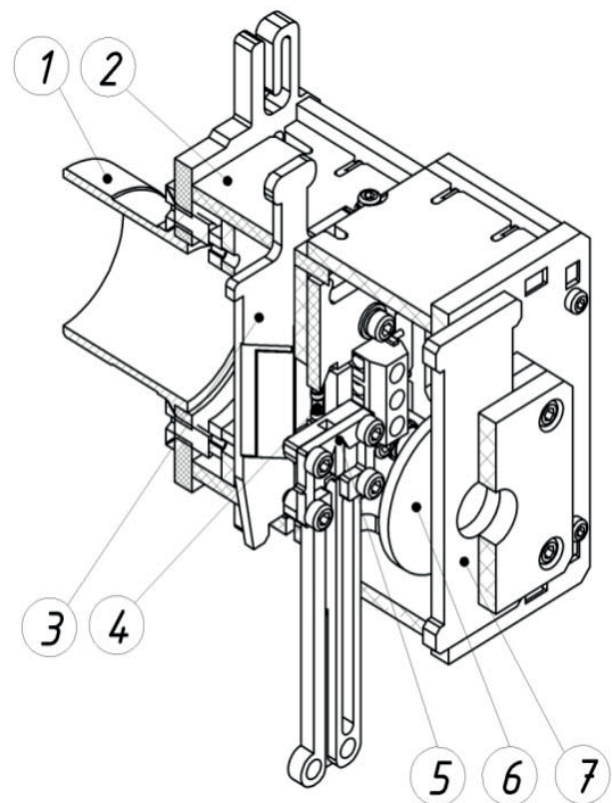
Устройство сенсорной головки (разрез): 1 – посадочная втулка 1.25"; 2 – корпус сенсорной головки; 3 – сменная цель; 4 – сенсорный резистор; 5 – монтаж платинового термометра; 6 – окуляр; 7 – шторка окуляра.
